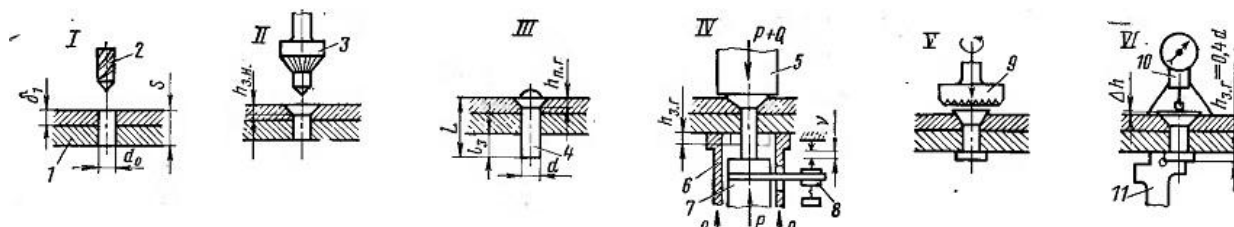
1 — склепываемый пакет; 2 — сверло; 3 — зенковка; 4 — заклепка ЗУК; 5 — верхний пуансон; 6 — прижим; 7 — нижний пуансон; 8 — система микровыключателей; 9 — торцевая фреза; 10 — индикатор с подставкой; 11 — шаблон
